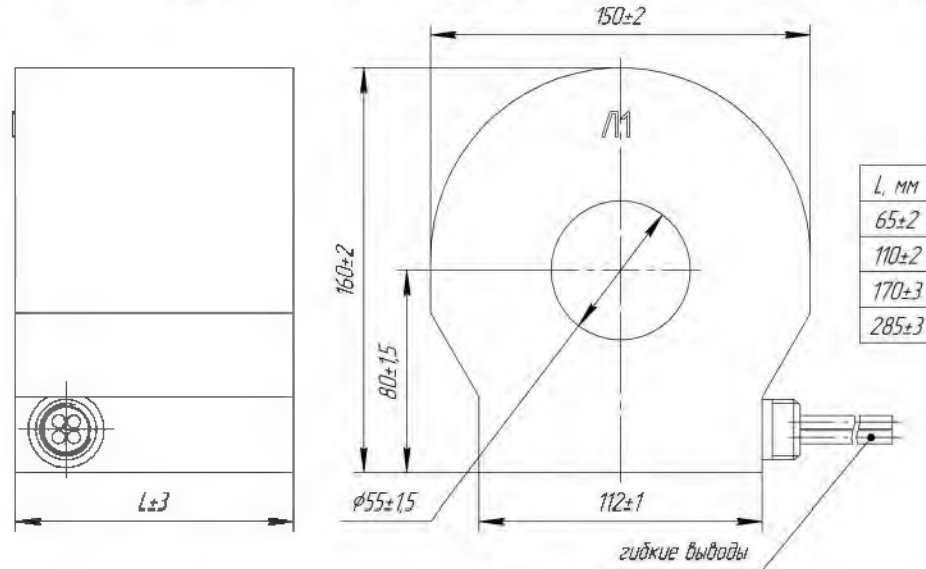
Габаритные и установочные размеры трансформатора тока ТП-ЭК-0,66 М4.
